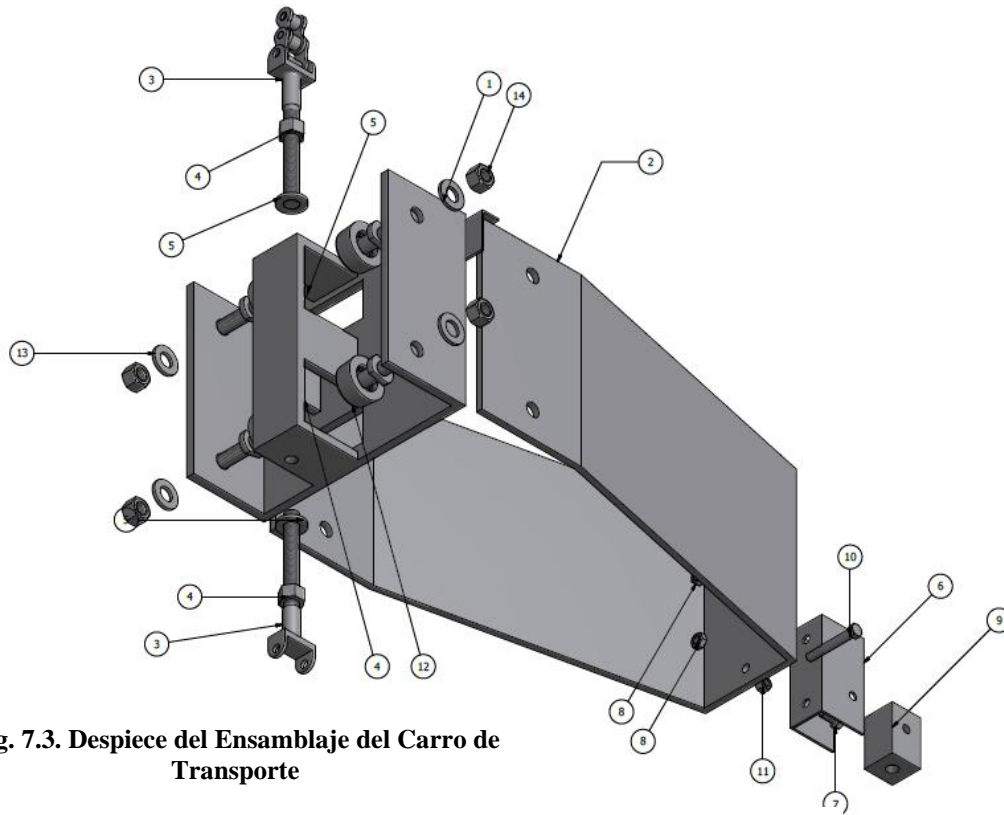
Despiece del Ensamblaje del Carro de Transporte
